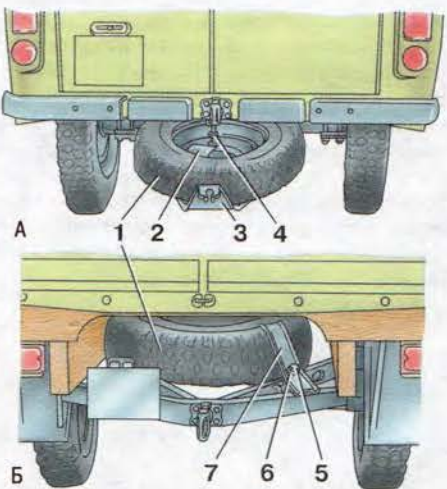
Крепление запасного колеса: А – автомобили УАЗ-374195, -396255, -390995, -220695; Б – автомобили УАЗ-330395, -330365, -390945; 1 – запасное колесо; 2 – сектор; 3 – держатель; 4 – гайка; 5 – болт; 6 – шайба; 7 – кронштейн
